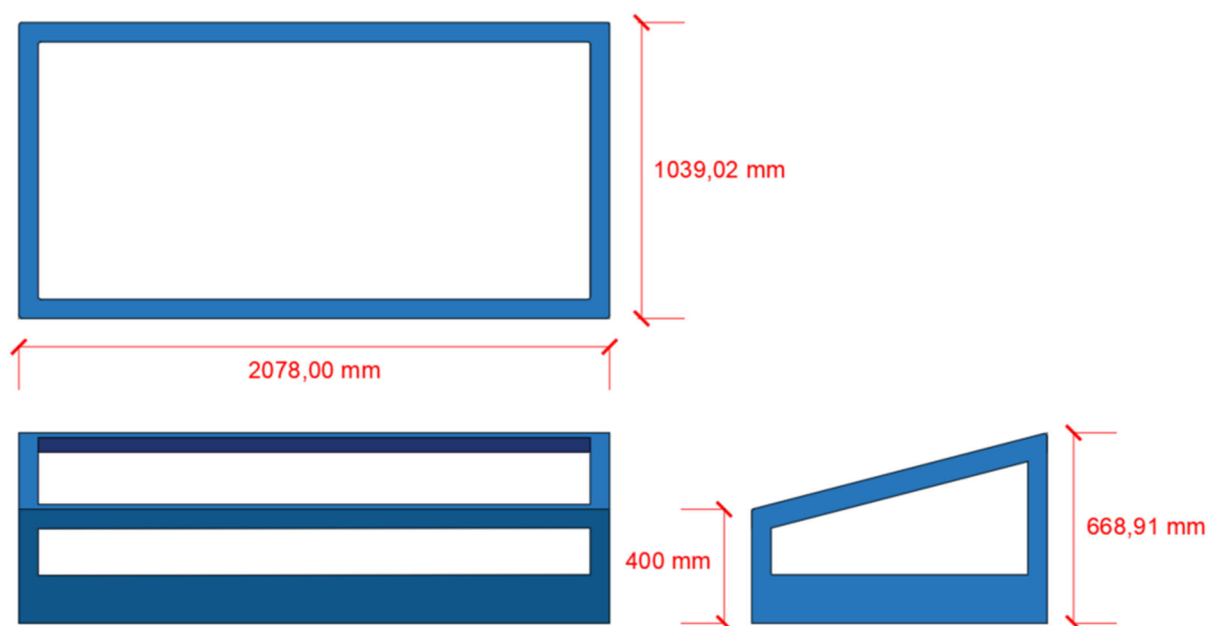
Vistes de l'estructura flotant (Font: Pròpia).
